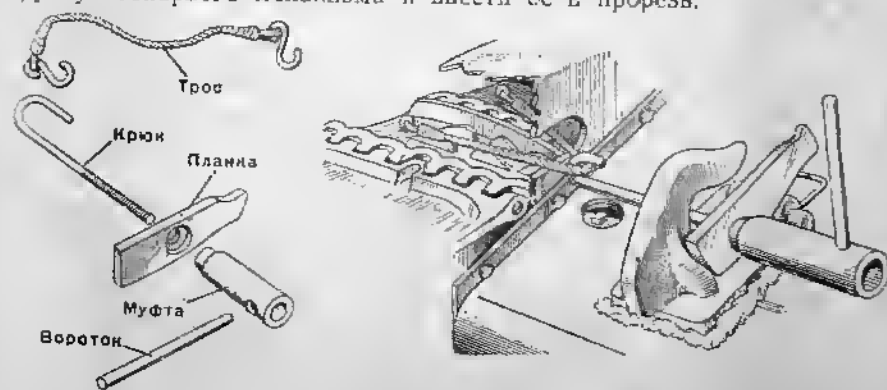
Введение кривошипа ленивца в зацепление при помощи приспособления
